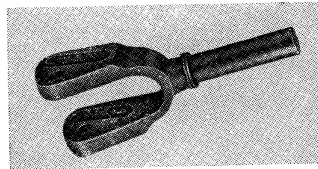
Вилка тяги. Сталь. Сварено трением (поковка + прокат). Диаметр стержня 30 мм
